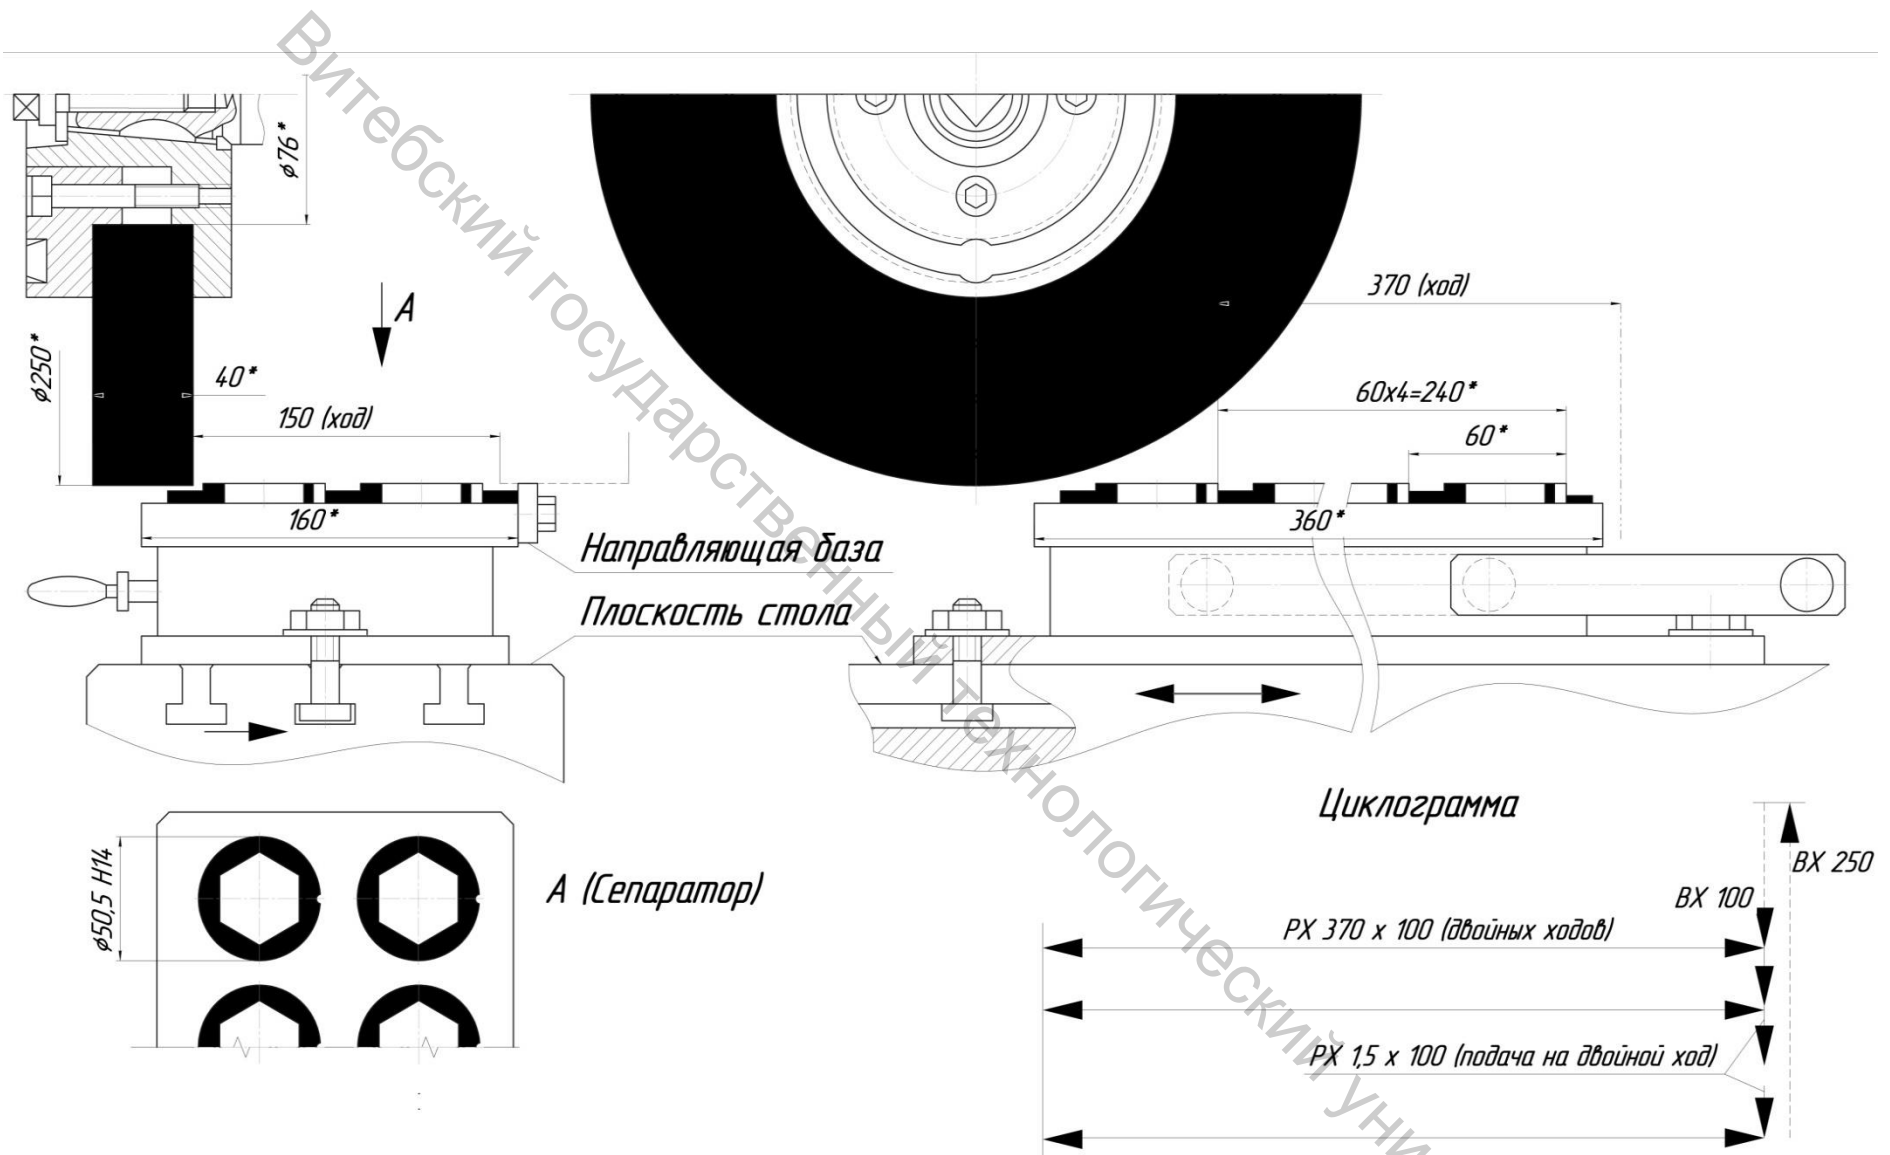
Схема наладки плоскошлифовального станка модели 3Е711 на обработку заготовки детали «Кольцо»
